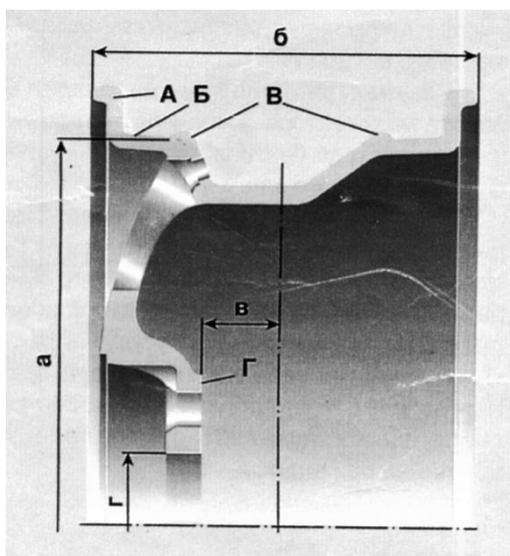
Основные элементы и размеры легкосплавного колеса:
